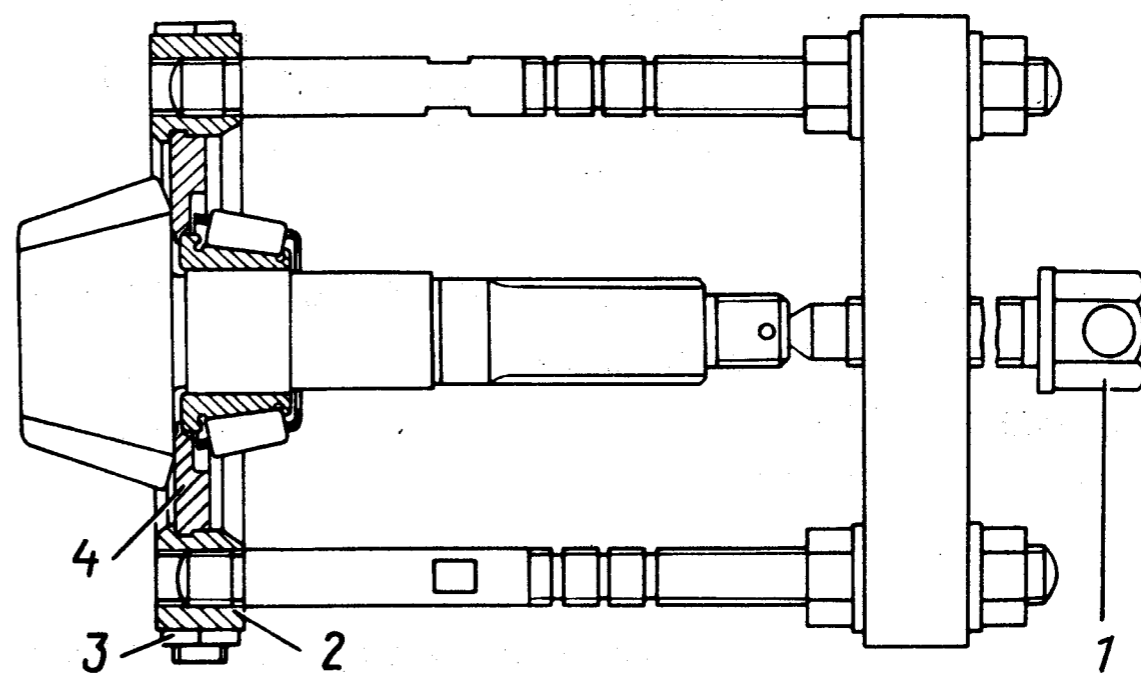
Снятие подшипника с ведущей шестерни главной передачи:
